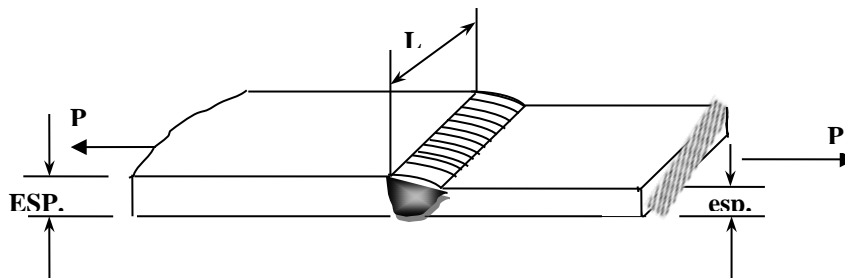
Soldadura a tope, de dos láminas de distinto espesor, sometidas a tracción.
